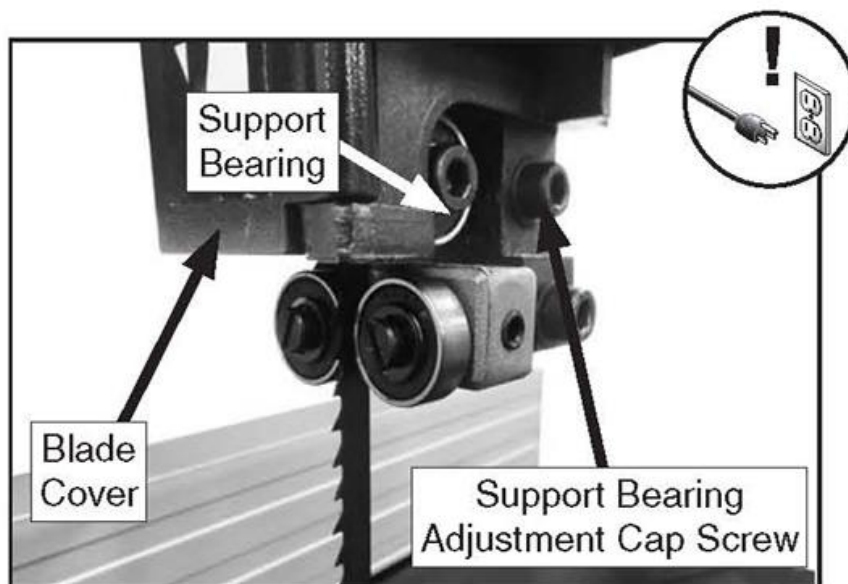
Верхний опорный подшипниковый узел и органы управления.
